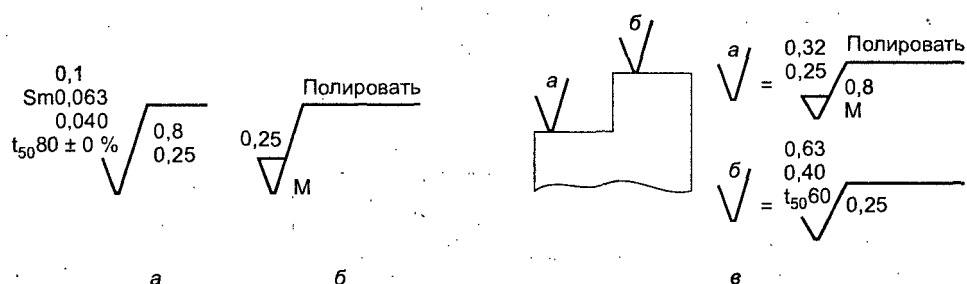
Примеры обозначения шероховатости на чертежах
